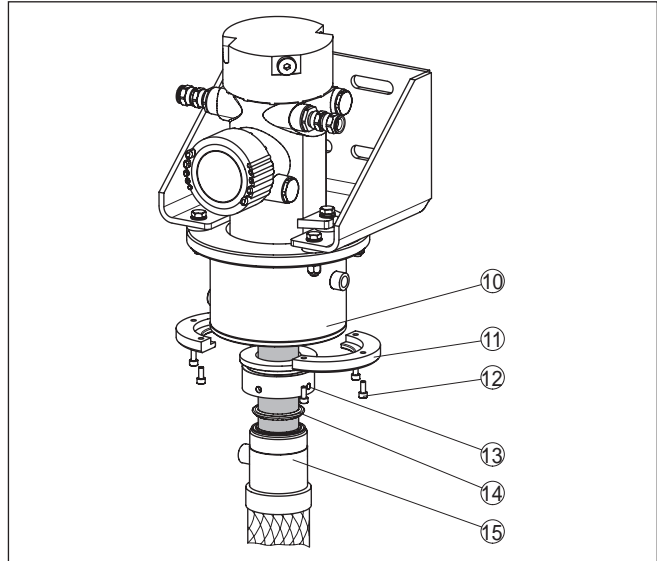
Montagem da refrigeração do cintilador - parte superior
